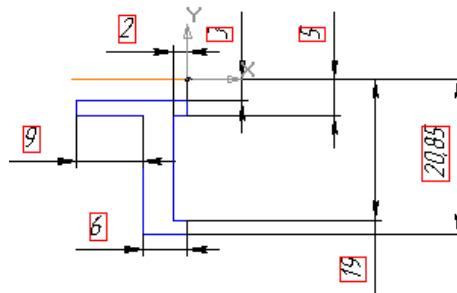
Ескіз заготовки зубчастого колеса
